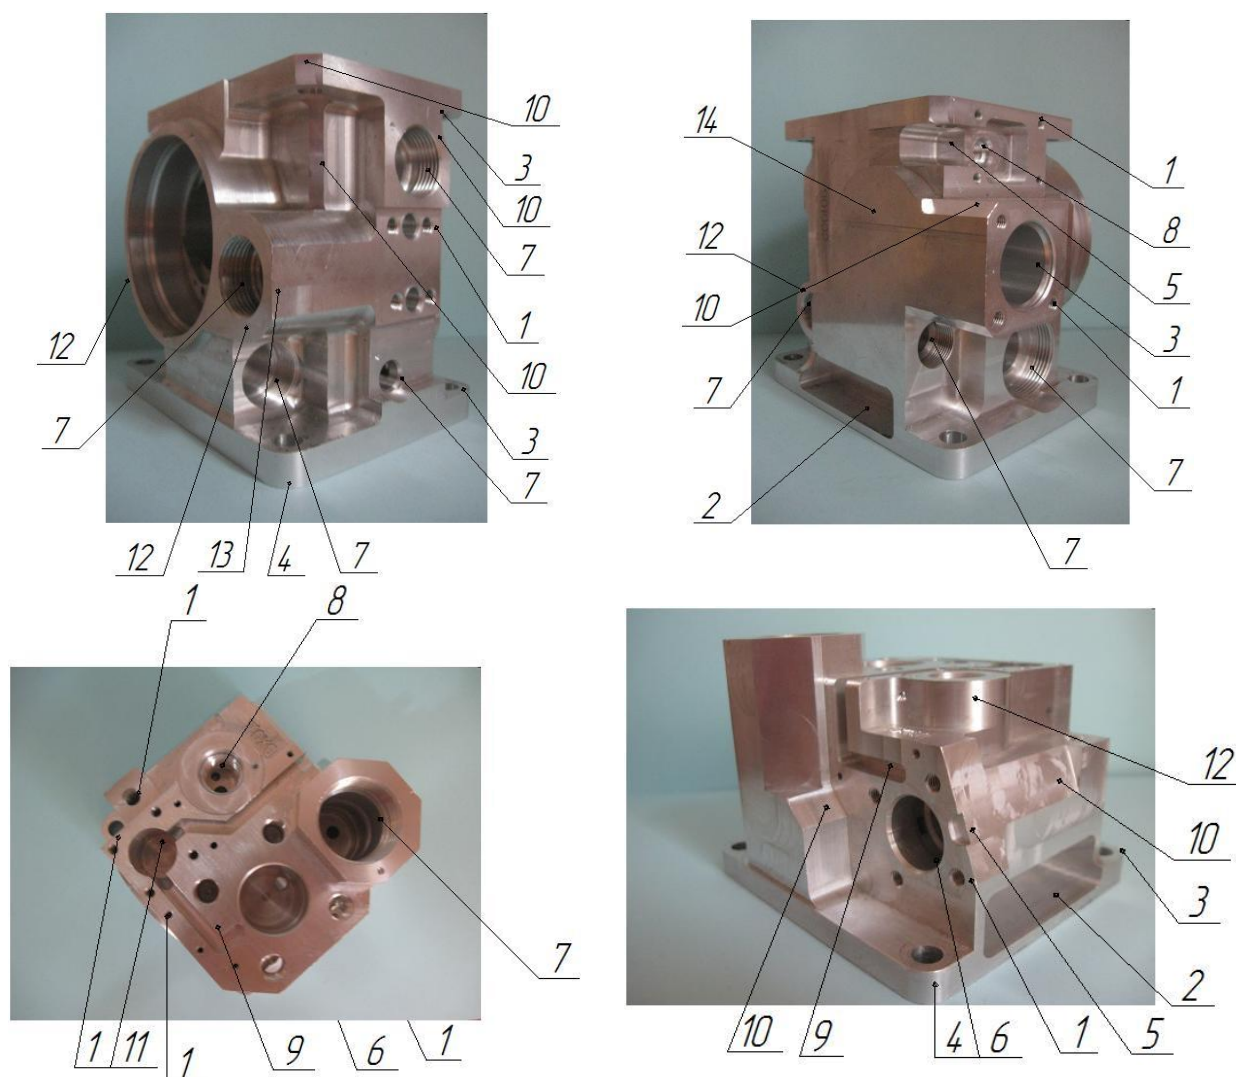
Виды и особенности конструкции деталей «Корпус»: 1, 3, 6, 7, 8, 11, 15 – цилиндрические отверстия различных диаметров; 2 – ниша; 4 – радиусные сопряжения прямолинейных поверхностей; 5 – горизонтальный «U» – образный паз; 9 – канавка сложнопрофильная; 10 – уклон; 13 – лыска; 14 – сопряжения прямолинейных плоских и криволинейных радиусных поверхностей
